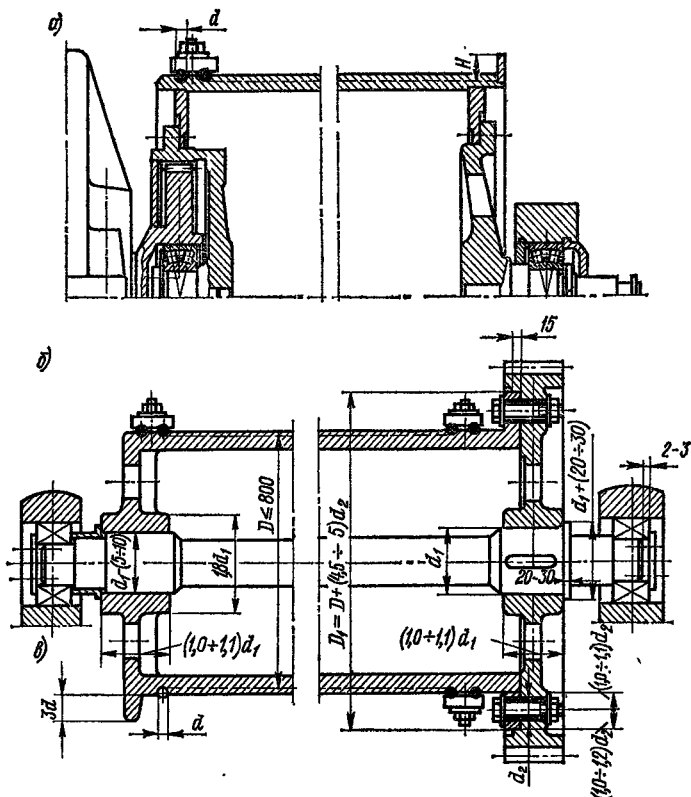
Барабаны: *a* — сварной с зубчатой муфтой ( $H > 3d$  при нормальной и  $H \geq 5d$  при глубокой канавке и канате диаметром  $d$ ); *b* — литой с зубчатым венцом при креплении двух концов каната на барабане; *c* — литой с зубчатым венцом при креплении одного конца каната на барабане
